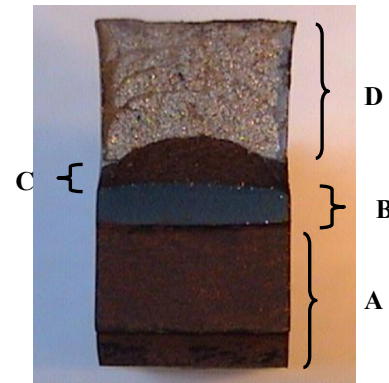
Vista Transversal de una probeta fracturada de Tenacidad a la Fractura Zona A : Zona mecanizada. Zona B : Fisura por Fatiga Zona C : Crecimiento de fisura. Zona D : Zona fracturada
